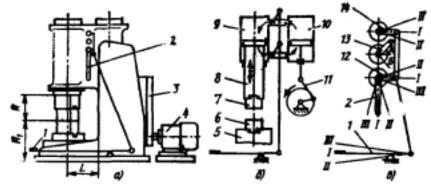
Пневматический молот: 1 — педаль; 2 — ручка управления молотом; 3 — передаточный механизм; 4 — электродвигатель; 5 — шабот; 6 — нижний боек; 7 — верхний боек; 8 — поршень-баба; 9 — рабочий цилиндр; 10 — компрессорный цилиндр; 11 — кривошип;
